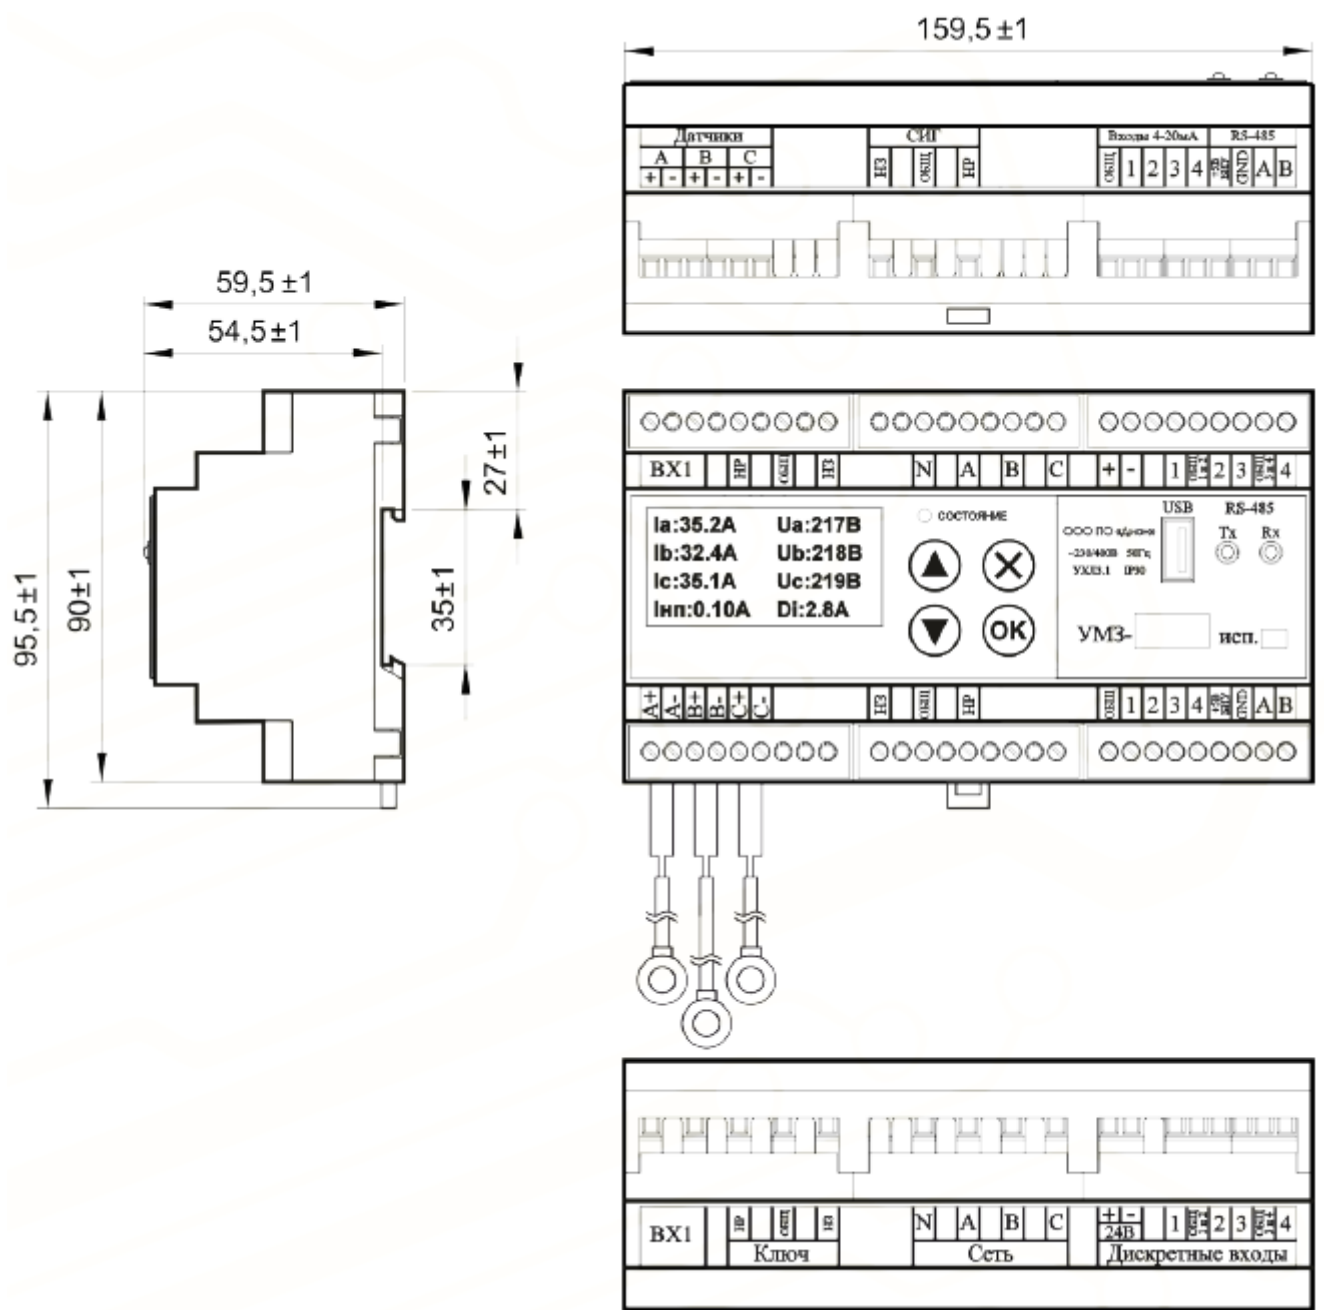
Габаритные и установочные размеры для устройств исполнений 32, 53 и 132
